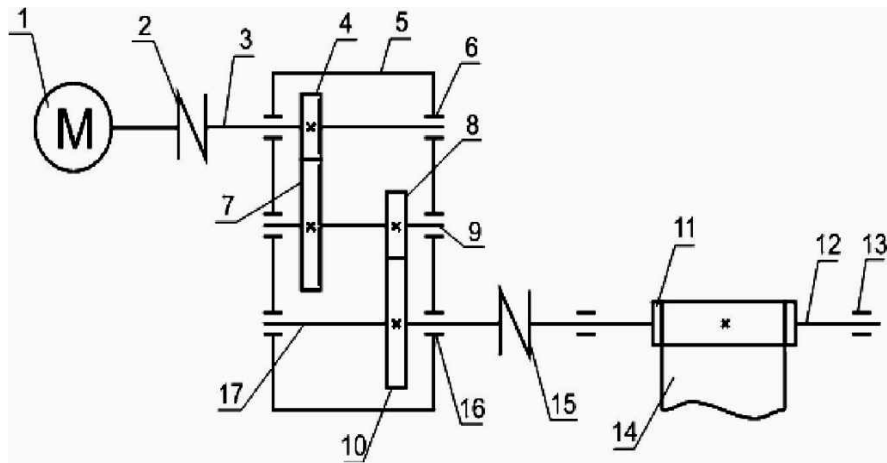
Привід до стрічкового конвеєра: 1 – електродвигун; 2,15 – муфти (МУВП, ланцюгова); 3 – швидкохідний (провідний) вал; 4,7 -1-ий зубчастий ступінь; 5 – корпус; 6,9,16 – підшипникові вузли; 8,10 - другий зубчастий ступінь; 11 - приводний барабан; 12 – вал; 13 - підшипниковий вузол; 14 – конвеєрна стрічка; 17 - тихохідний (відомий) вал
